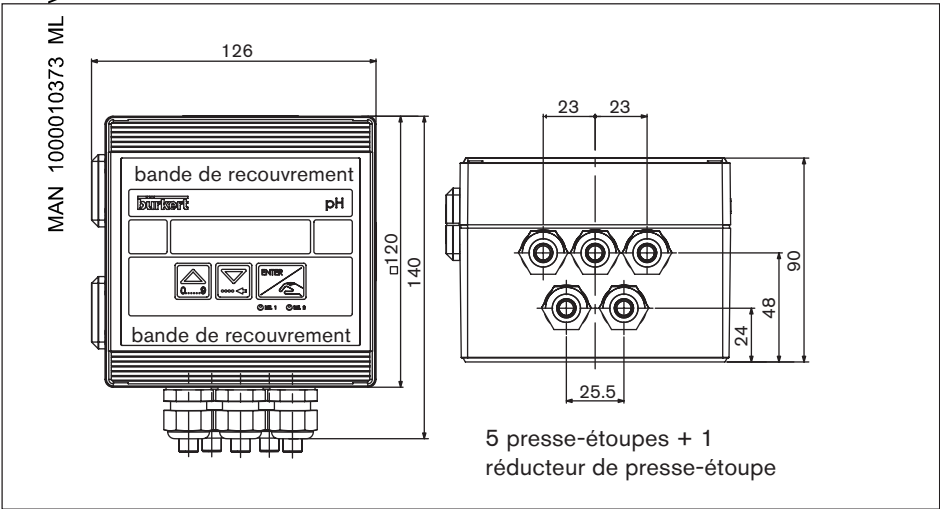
Dimensions régulateur de pH 8205 mural
